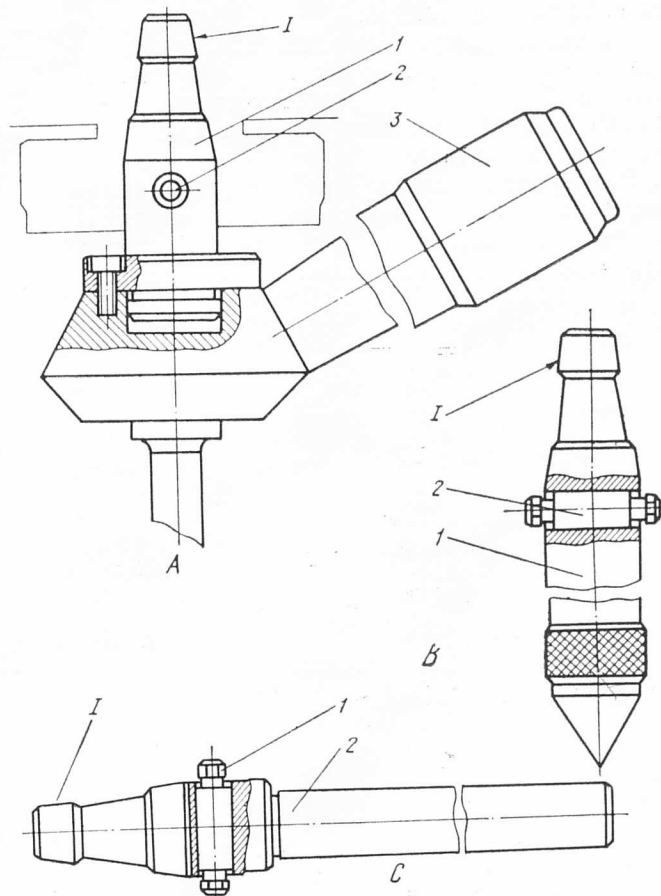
Основные шпиндельные принадлежности для взаимной выверки электрода-инструмента и обрабатываемой детали
